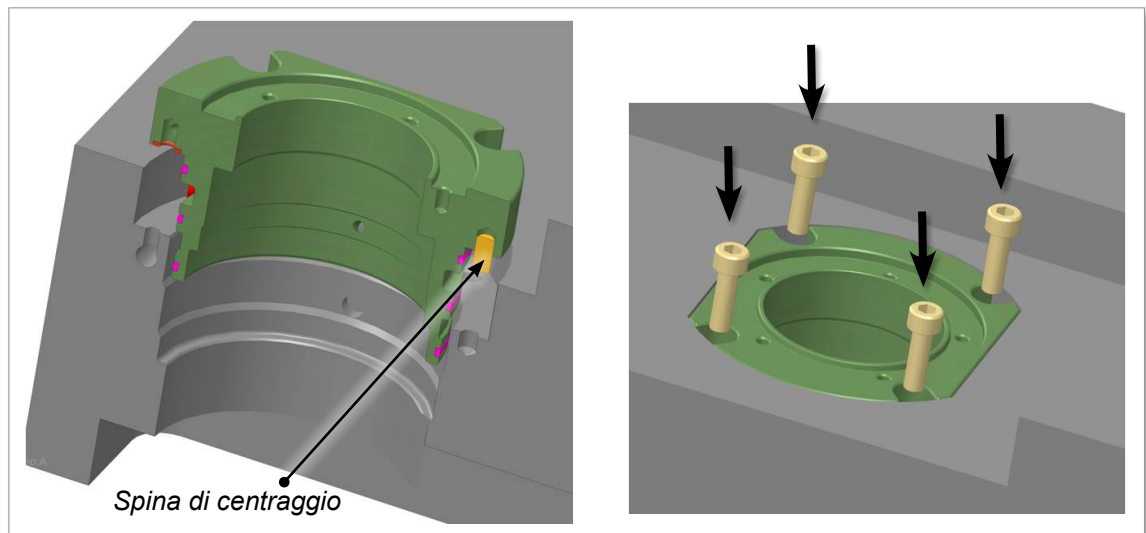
Fissaggio del corpo esterno alla piastra del collettore.
